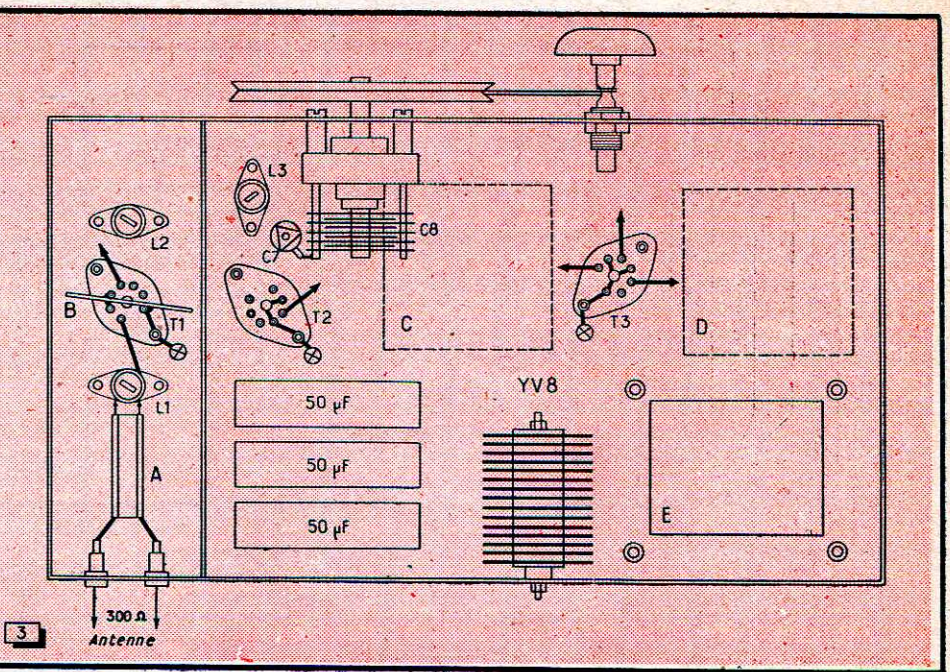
Disposition des pièces principales : A : arrivée d'antenne à 300 Ω (morceau de descente bifilaire); B : écran soudé au support de lampe; C : emplacement du transformateur M.F.;
